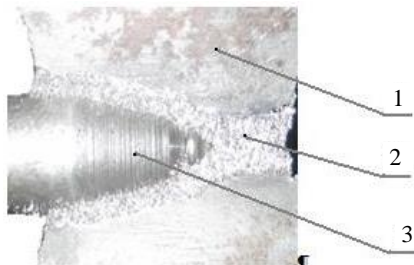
Вид рабочей зоны при МАО резцов РКС1: 1 – полюсный наконечник; 2 – ферроабразивная щетка; 3 – поворотный резец
